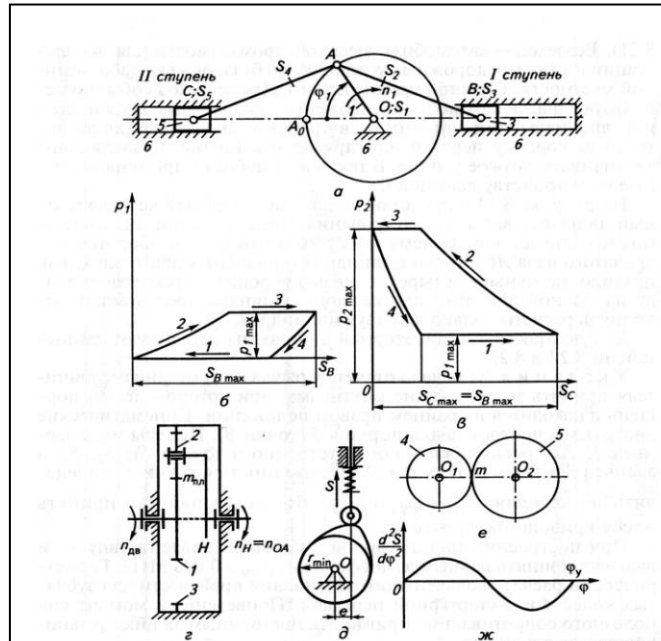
Механизмы двухступенчатого двухцилиндрового воздушного компрессора:
